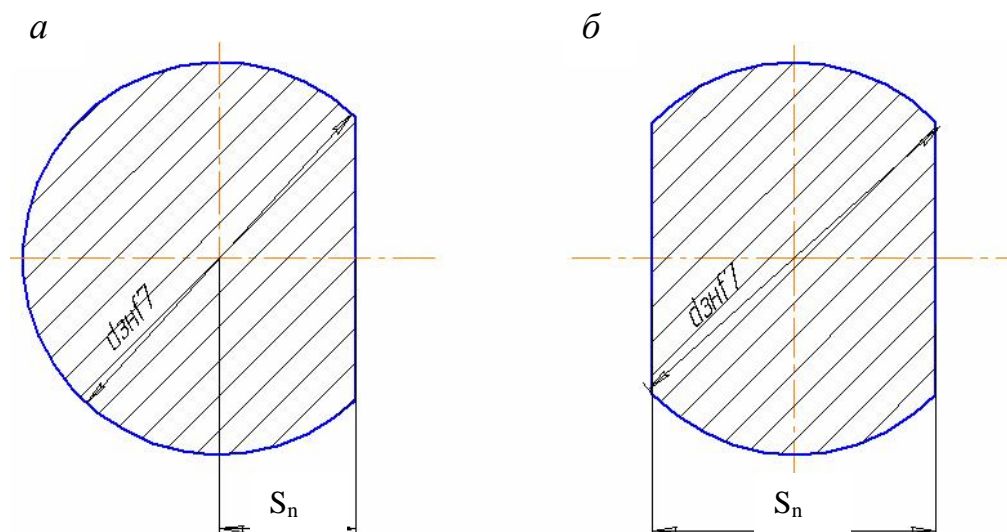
Профиль поперечного сечения задней направляющей протяжки:
